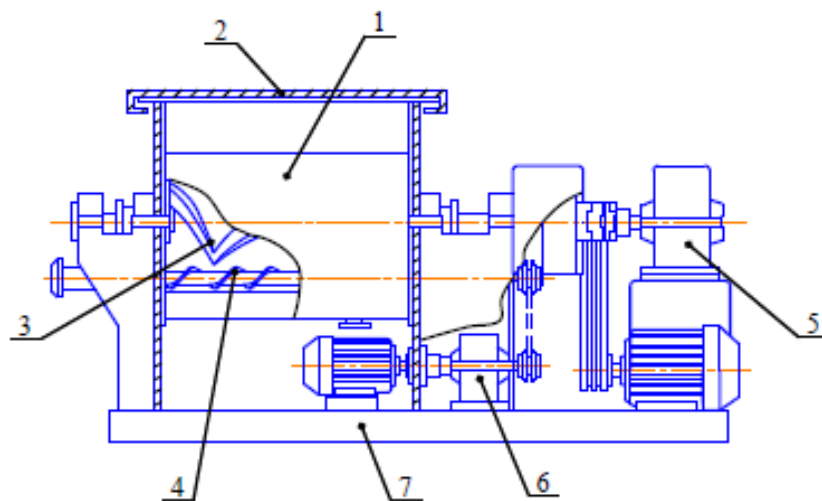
Двох лопатевий змішувач із реверсивним шнеком типу СРШ: 1 – камера змішування; 2 – кришка; 3 – валки; 4 – реверсивний шнек; 5 – привід валків; 6 – привід шнека; 7 – станина [1].
